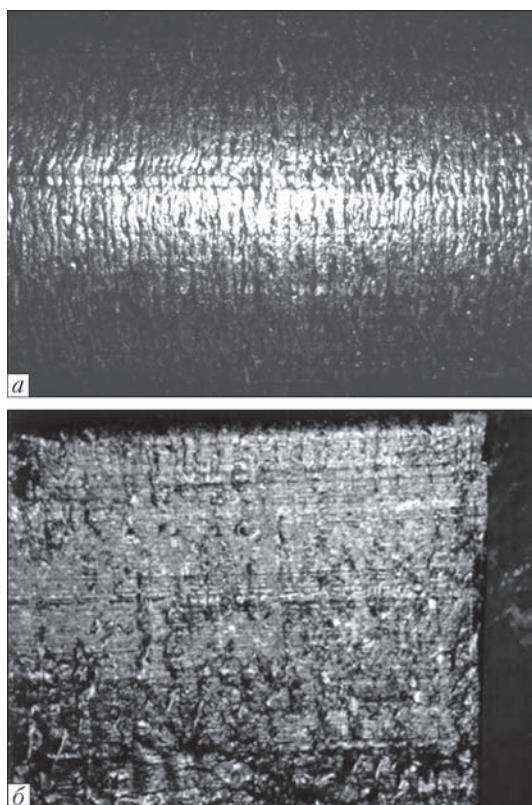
Внешний вид поверхности слитков ЭЛП: *а* — цилиндрического; *б* — прямоугольного сечения
